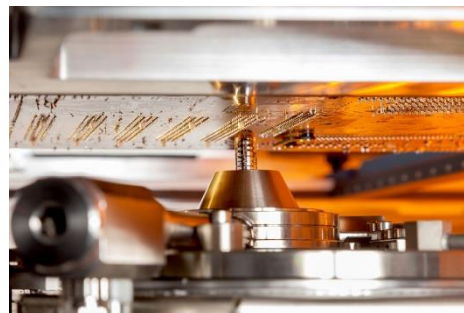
Soldadura selectiva multi ola, (Kurtz ursa, s.f.)
